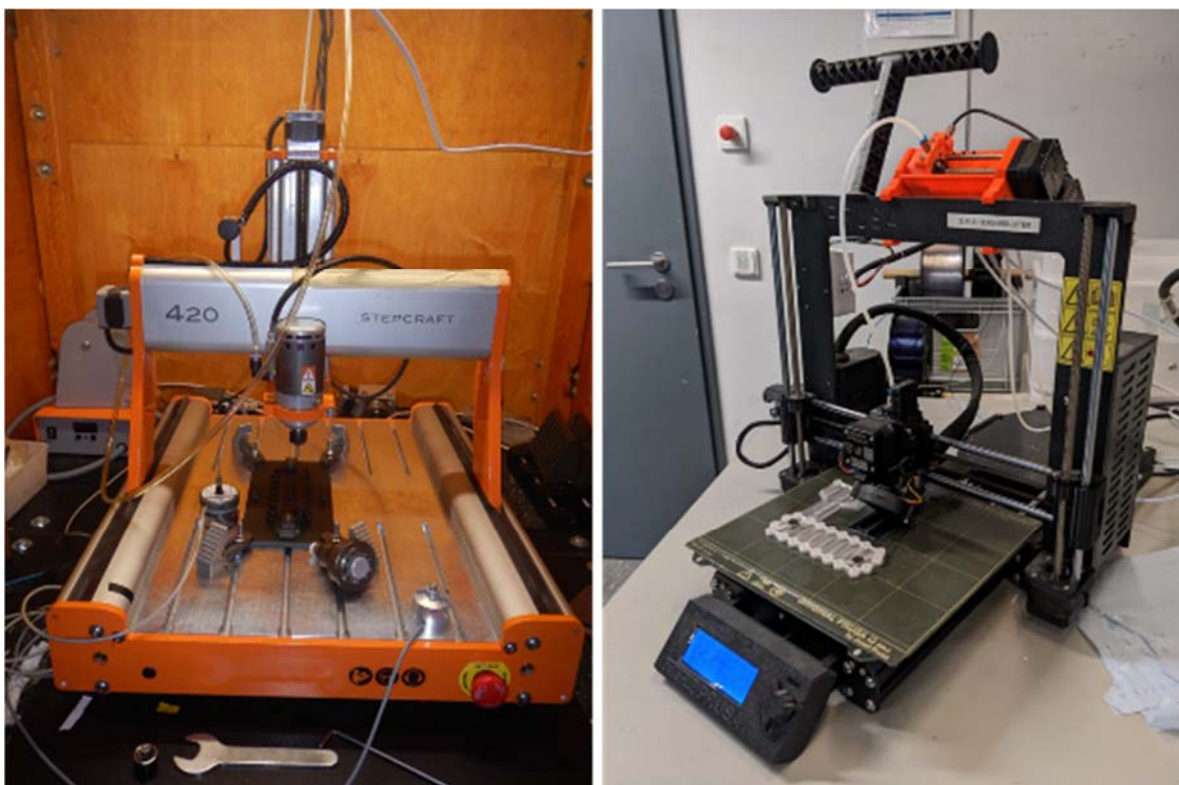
Für die Fertigung der passiven PEMFC eingesetzten Werkzeuge: Links) STEPCRAFT D420 CNC-Fräse mit Schleppmesser + 3D Taster; rechts) Prusa I3MK3S mit MMU2S 3D-Drucker
